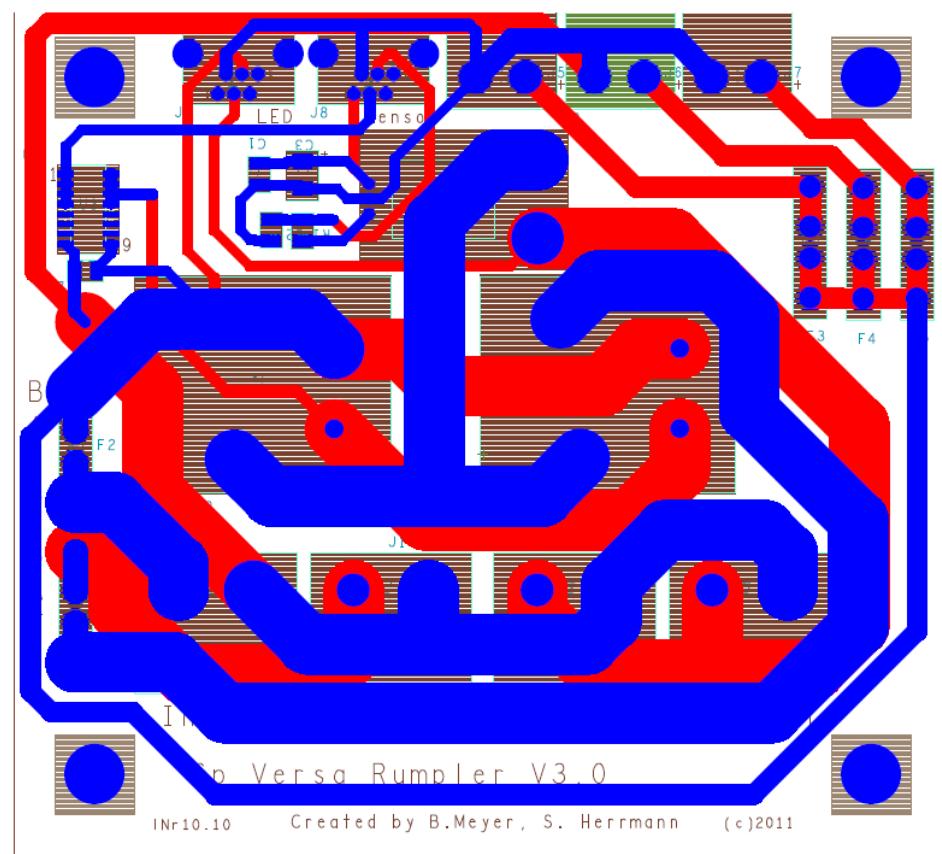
Layout für die Spannungsversorgungsplatine.
